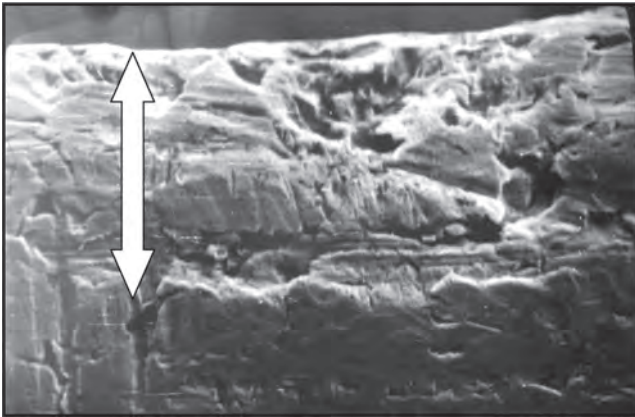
Разрушение кромки образца из ЧПГ марки СЧ30.  $\times 500$
